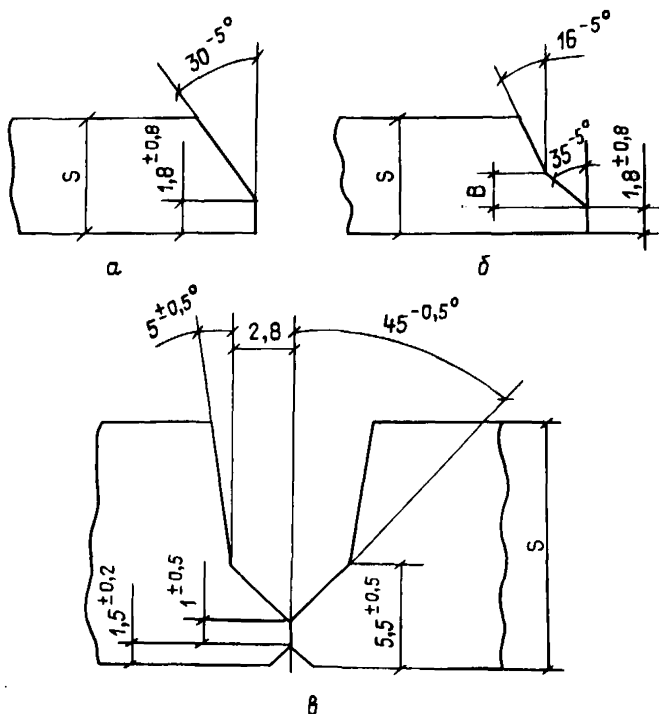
Типы разделки кромок труб для ручной дуговой сварки, односторонней автоматической сварки под флюсом, автоматической дуговой сварки порошковой проволокой с принудительным формированием, полуавтоматической сварки в защитных газах: а — для труб D 57–1420 мм с толщиной стенки до 16 мм; б — для труб D 273–1420 мм с толщиной стенки более 15 мм; в — для автоматической сварки труб в защитных газах
